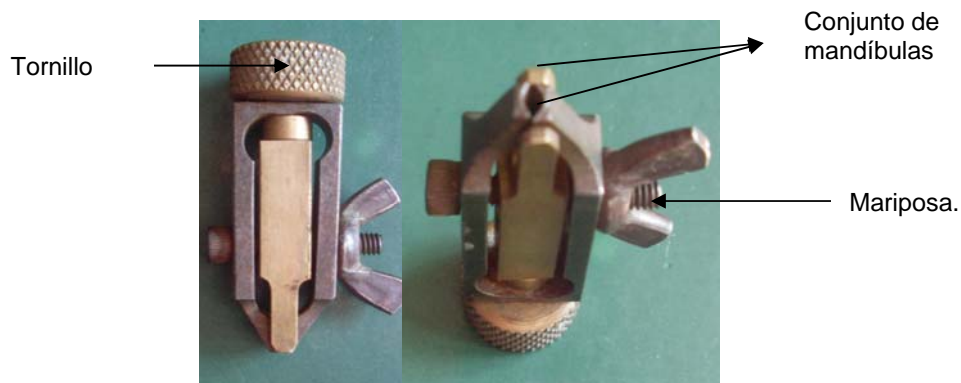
Partes del extractor de Egger, que también es conocido como "Pequeño Gigante"
